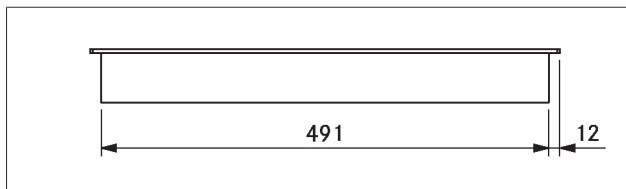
Dimensões do aparelho CKI, vista lateral
